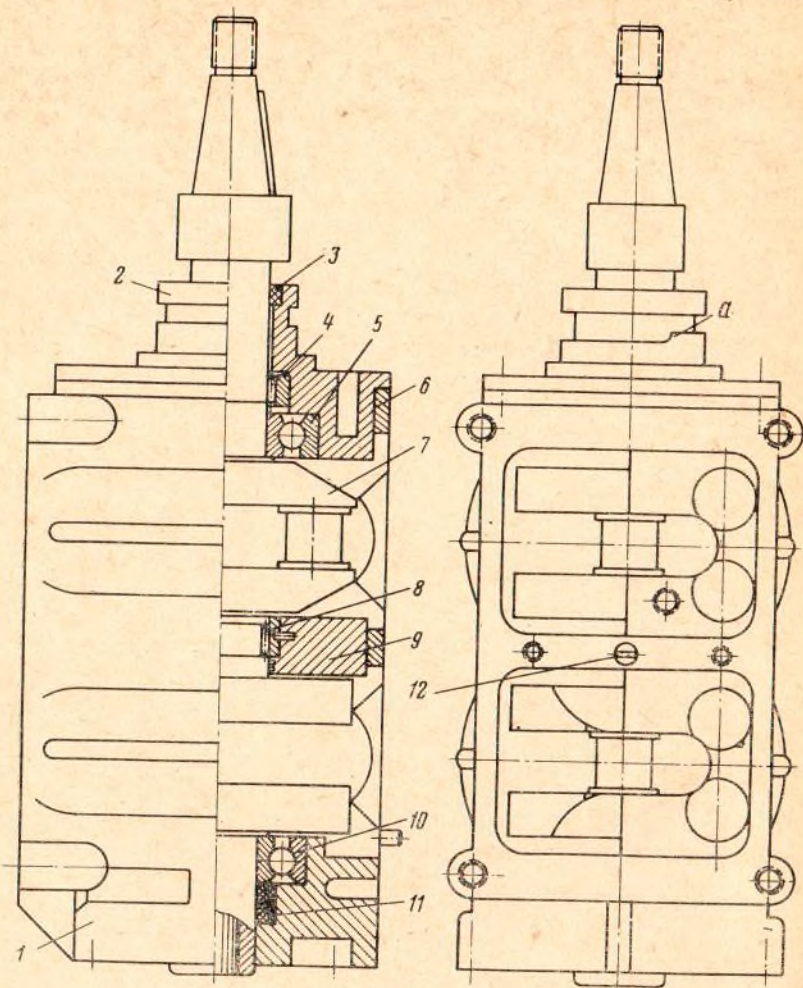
Картер тоннельной конструкции в сборе с коленчатым валом
